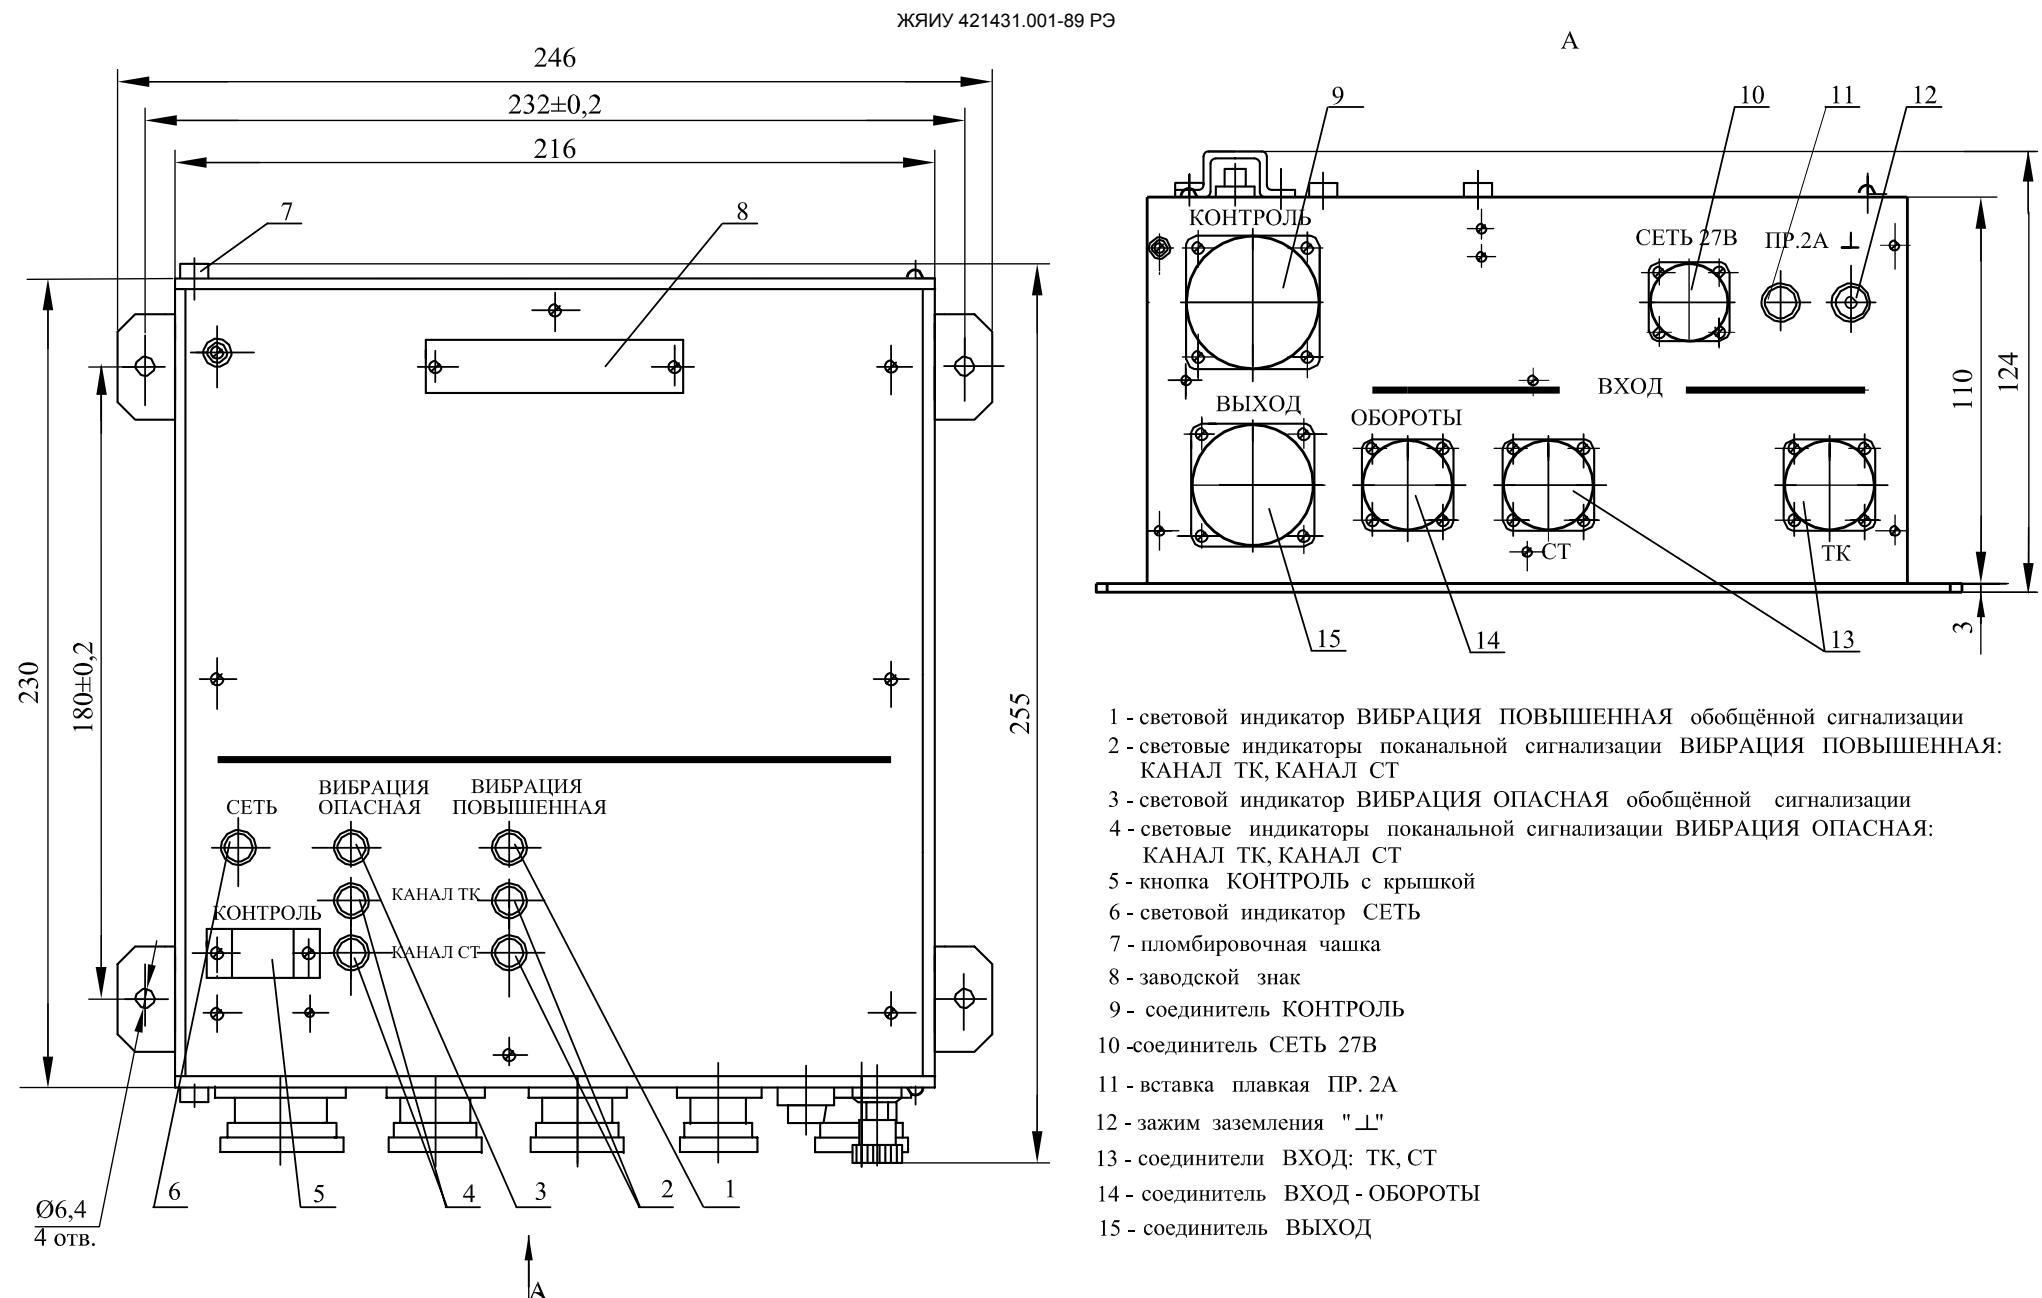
Габаритно-установочные размеры блока БЗ-38-1М.3.2-01
